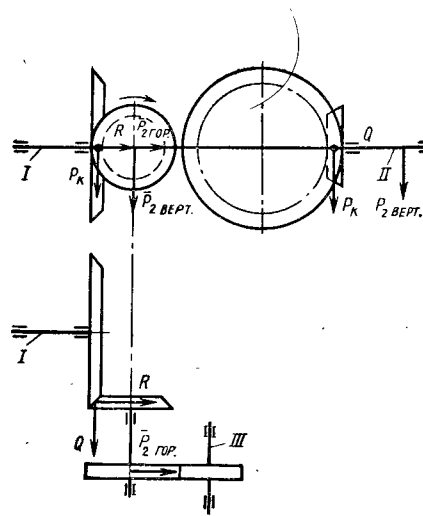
Схема нагружения валов силами, действующими в зацеплении конических шестерен коробки передач трактора Т-74 (вид со стороны двигателя):
